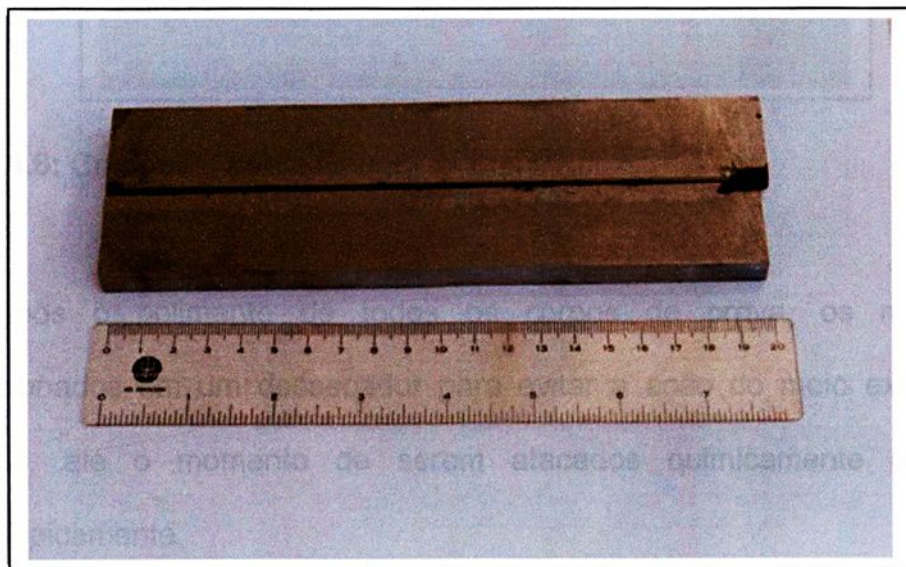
Detalhe da região mais clara do corpo de prova (metal de solda) onde observa-se o entalhe.
